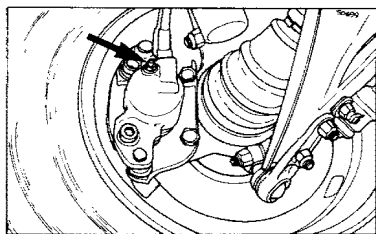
17 Штуцер для прокачки на суппорте переднего колеса
